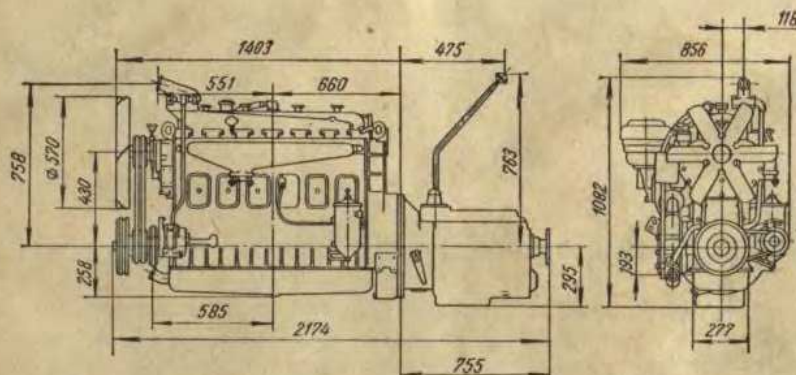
Габаритные размеры двигателя ЯАЗ-М206А
